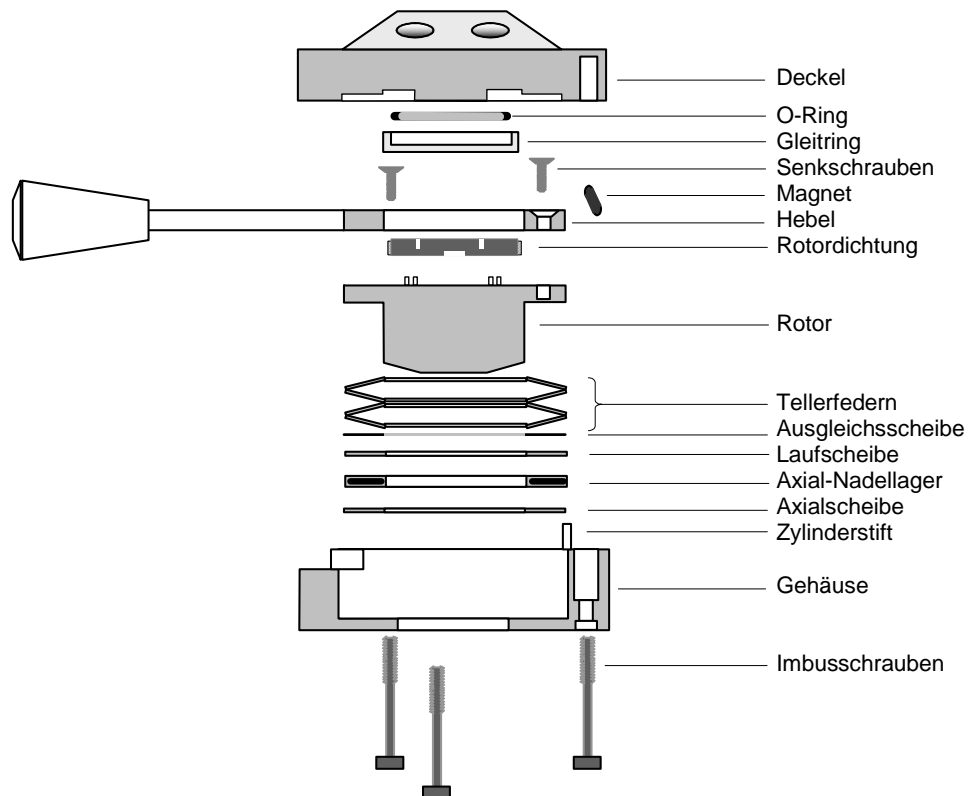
Explosionsdarstellung 6-Port-3-Kanalventil
